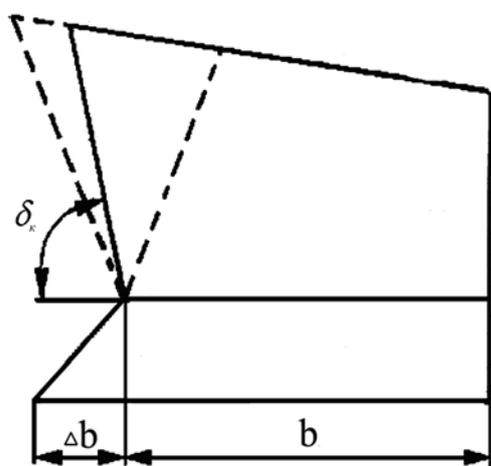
Схема построения бороздного обреза и изменения длины отвала выгребающего корпуса
